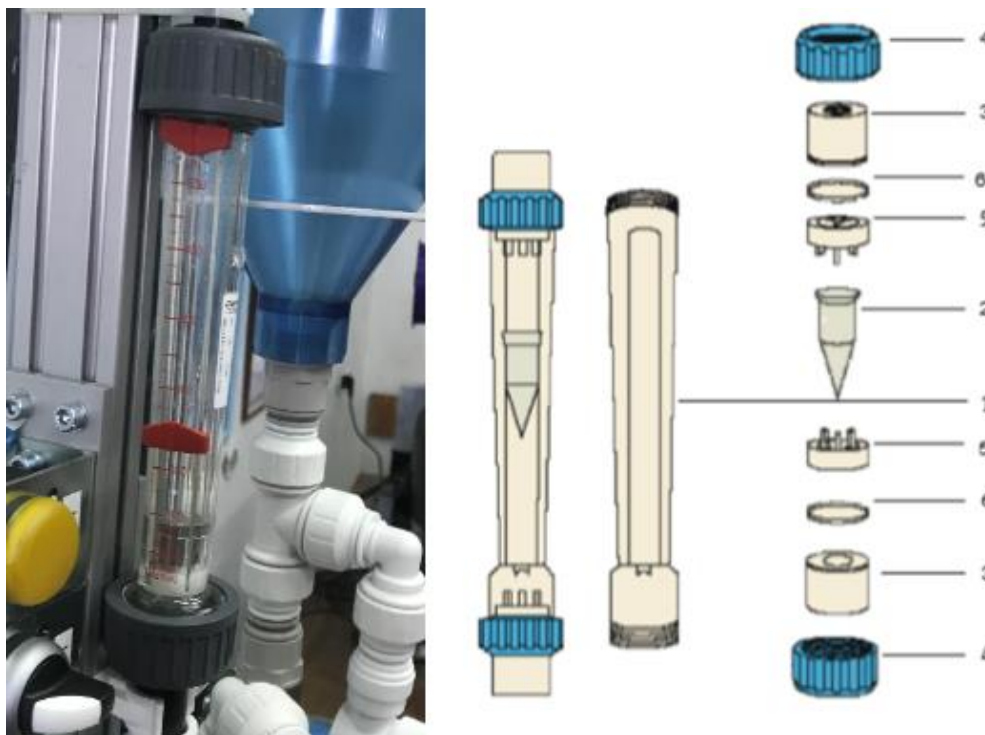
Конструкція та загальний вигляд ротаметра: 1- конічна трубка; 2- поплавок; 3 – різьбова втулка; 4 – ковпачок; 5 – патрубки; 6 – ущільнююче кільце;
